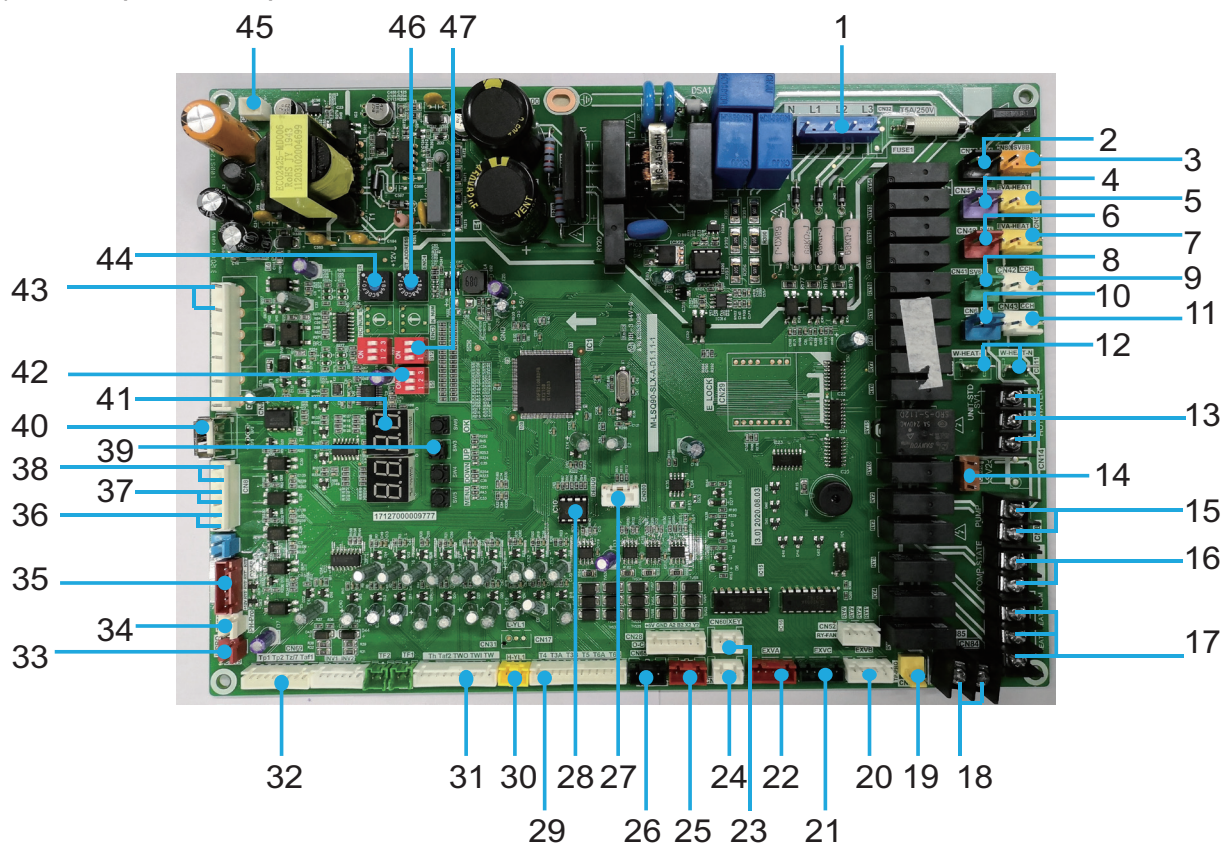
PCB principale du KEM-90 DRS5 KH et du KEM-180 DRS5 KH
